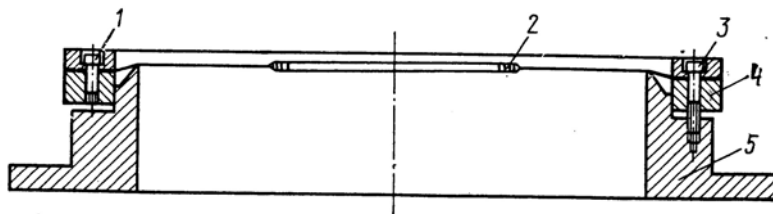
Схема механического способа натяжения круга: 1 – стягивающие винты; 2 – круг; 3 – регулирующие винты; 4 – кольца; 5 – барабан
